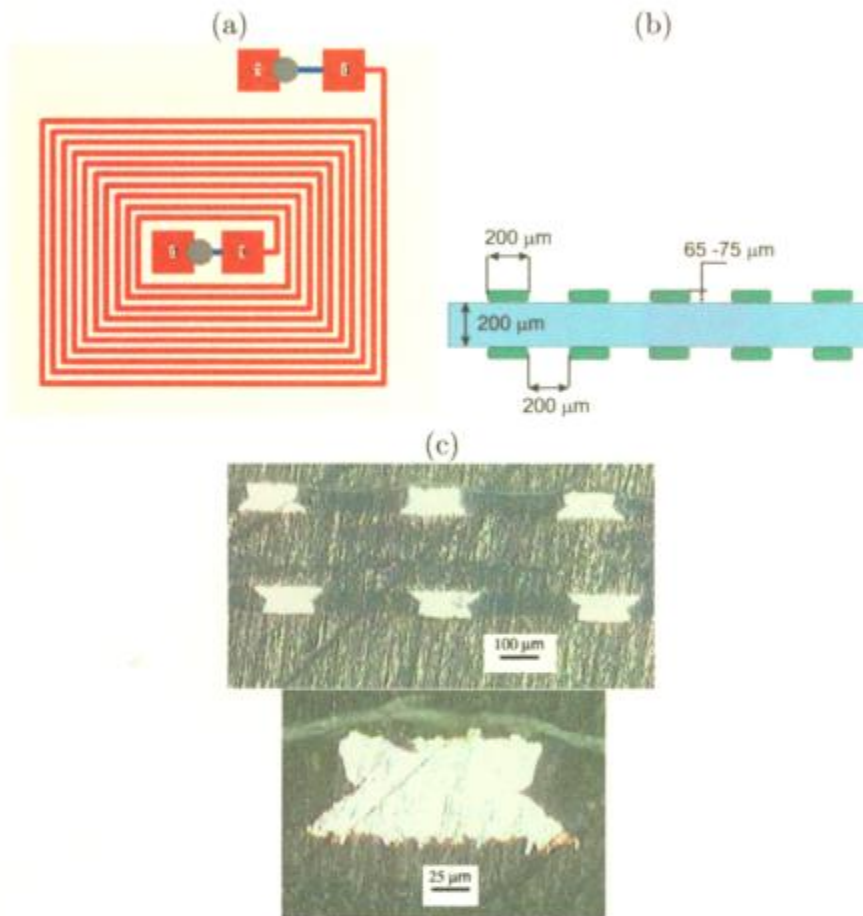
(a) Una bobina plana, el rojo indica el lado soldadura y el azul el lado de operación. (b) Vista en corte de una bobina plana, se indican las dimensiones características. (c) Corte de las bobinas fabricadas, se puede ver la forma resultante de los caminos y el espesor de la mascara antisoldante que protege y aísla a los caminos de cobre. Las fotos fueron tomadas en un microscopio óptico con ocular de 10X, la foto de arriba con un aumento de 5X y la de abajo con un aumento de 20X.
